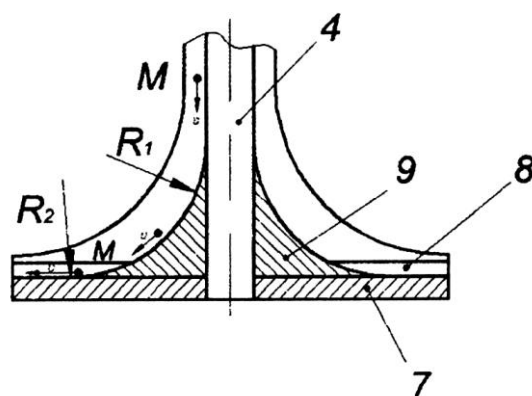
Разрез С-С конусного рассекателя, диска с радиальными лопатками и вала шнека
